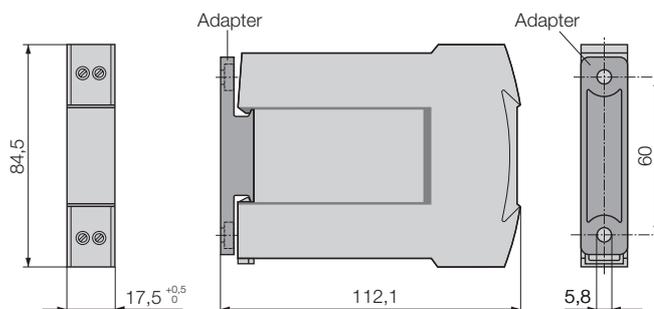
SINEAX SI 815-5... (N17-Gehäuse) mit Adapter für direkte
